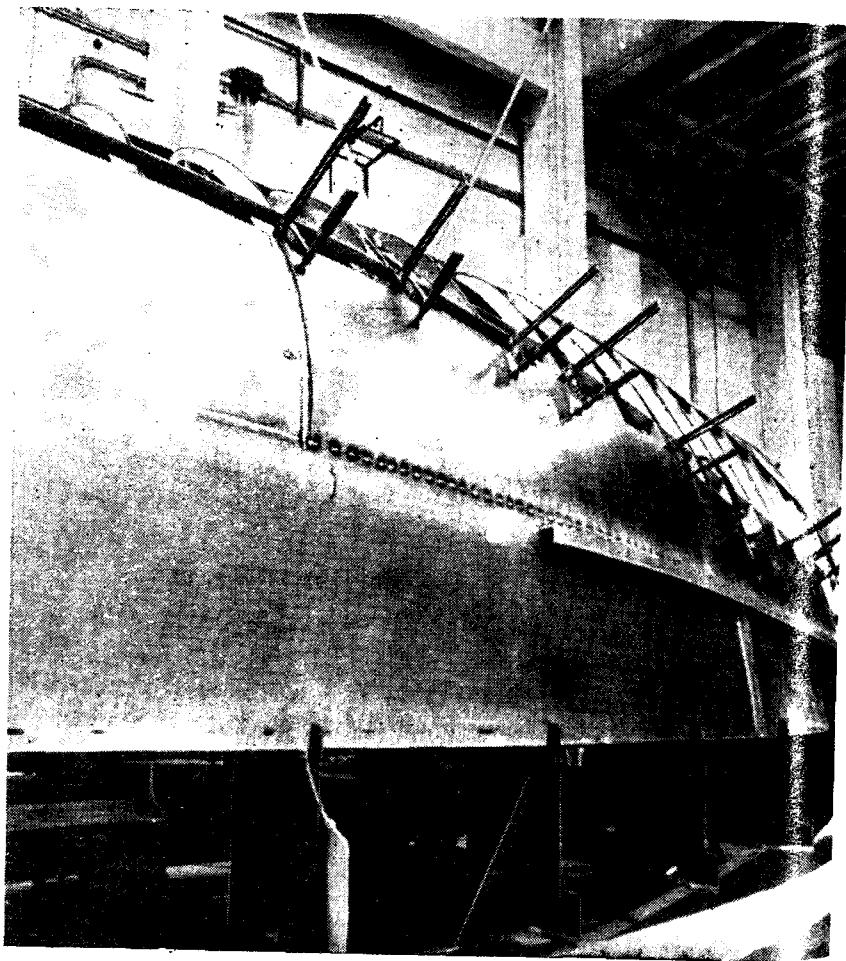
Последовательность сварки при монтаже листа наружной обшивки: после того как стык сварен полностью и выровнен, прихватывают точечной сваркой продольный шов. На время сварки обшивку к набору временно прижимают струбцинами.
